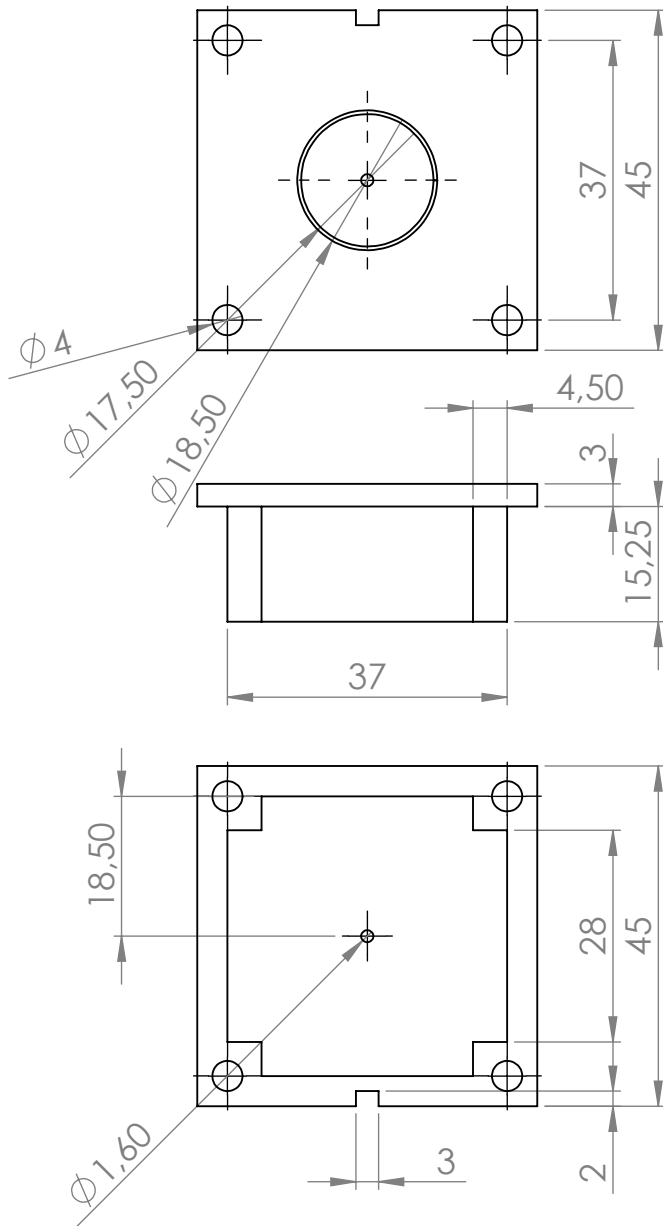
Diseño del molde para enmallado interno del *Robot Uniaxial* parte A
